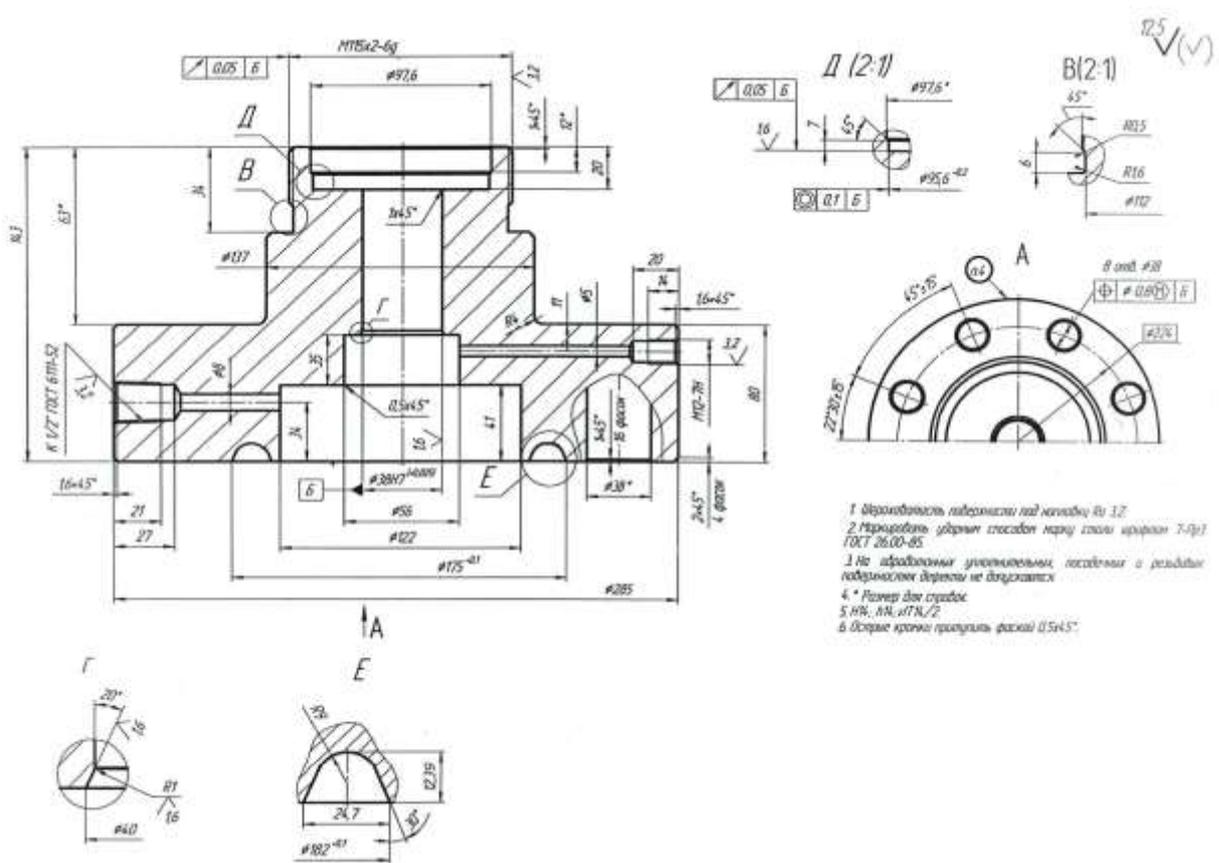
Эскиз детали «Крышка ЗШ 80x70-К2.016»
